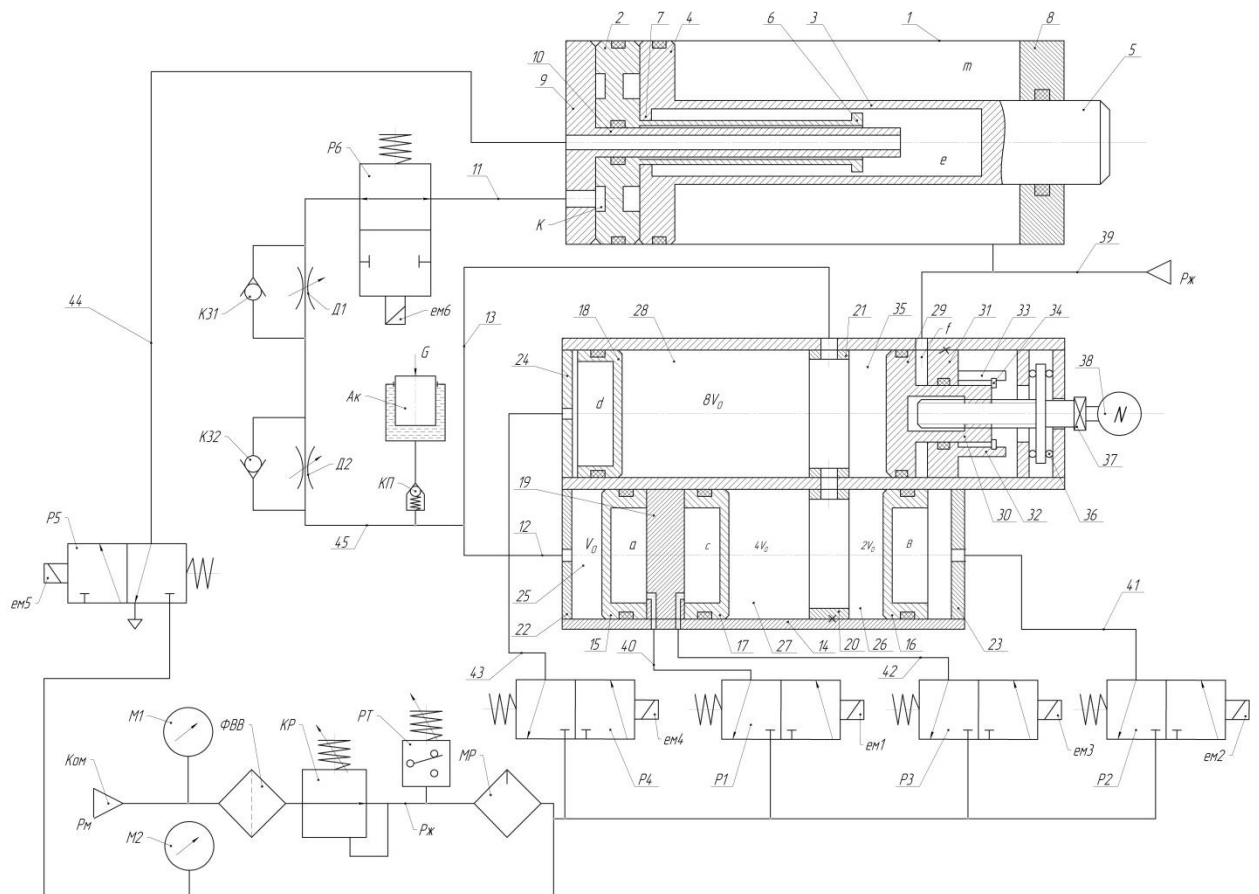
Принципова схема багатопозиційного приводу руки промислового робота.
